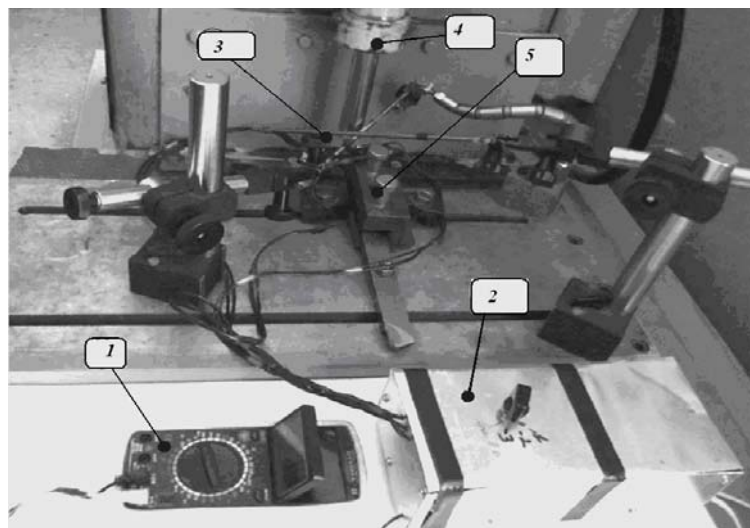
Фотография рабочей зоны стенда для испытания резцов на жесткость:
